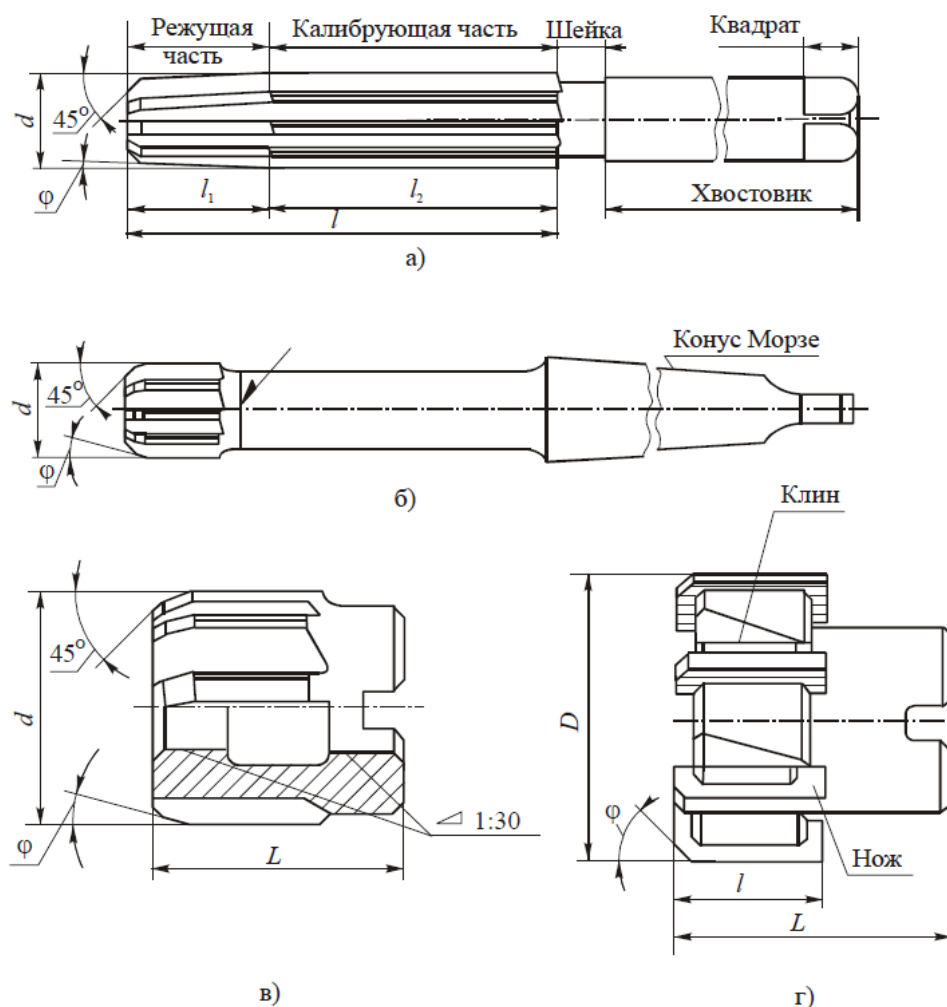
Типы цилиндрических разверток: а – ручная; б – машинная; в – насадная; г – сборная
